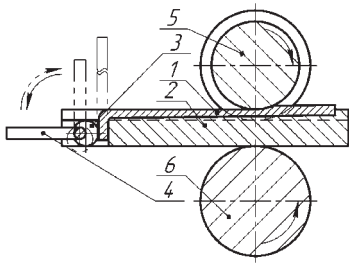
Схема прокатки полосы с рассогласованием окружных скоростей деформирующего инструмента и фиксацией конечного участка: 1 – заготовка; 2 – калибрующая оправка; 3 – кулачковый зажим; 4 – рычаг; 5 – верхний валок; 6 – нижний валок
